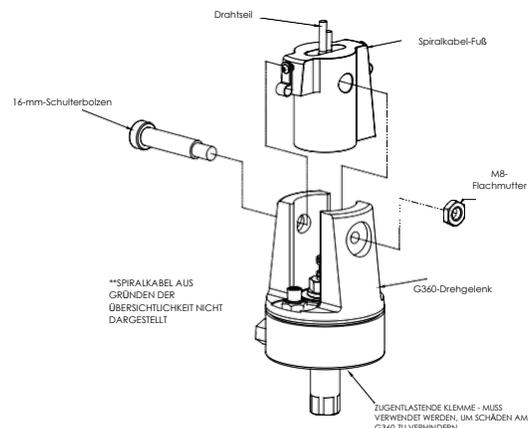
B1. G360™, Schulterbolzen und Spiralkabel
